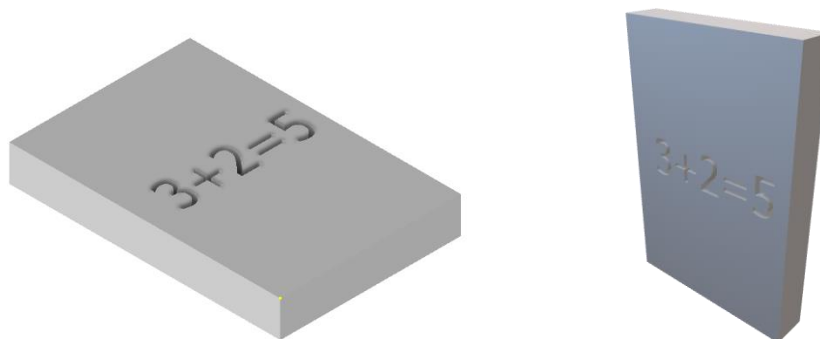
Τρισδιάστατη απεικόνιση αποστολής 38
